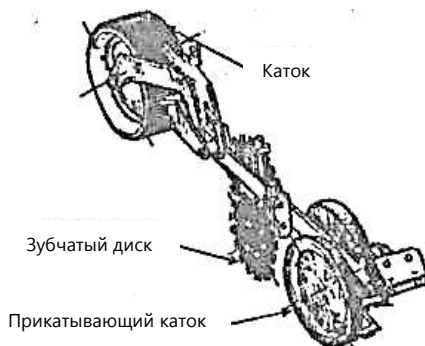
Дисковые сошники в сочетании с бороздными колесами
